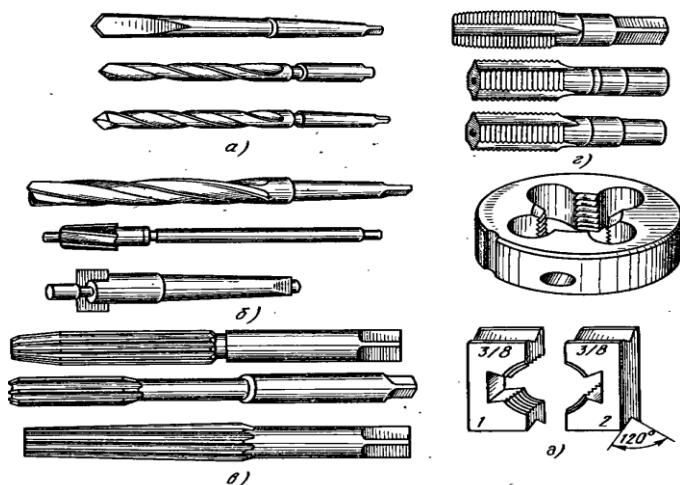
Осевые режущие инструменты: *а* — сверла (перовое и спиральные), *б* — зенкеры (цельный, насадной и с вставным ножом), *в* — развертки (ручная цилиндрическая, машинная цилиндрическая и конусная), *г* — метчики, *д* — плашки (круглая цельная и квадратная раздвижная)
